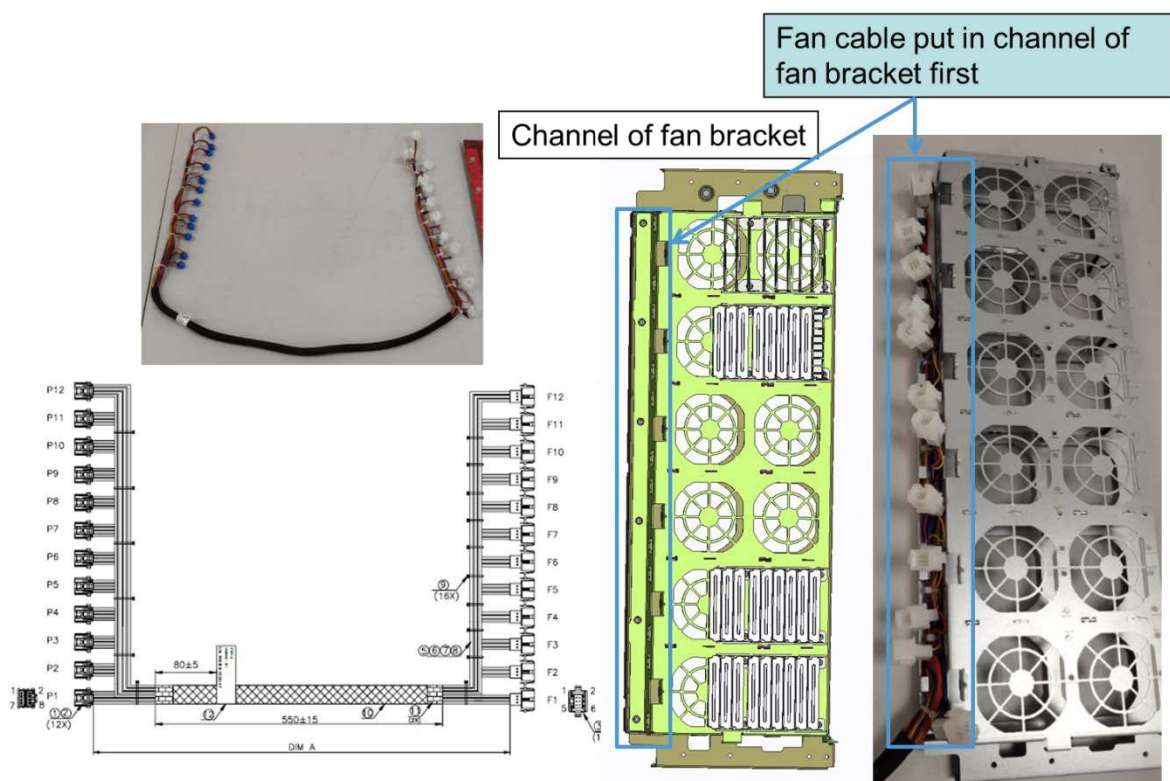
Assemblage du câble de ventilateur vers le support de ventilateur
